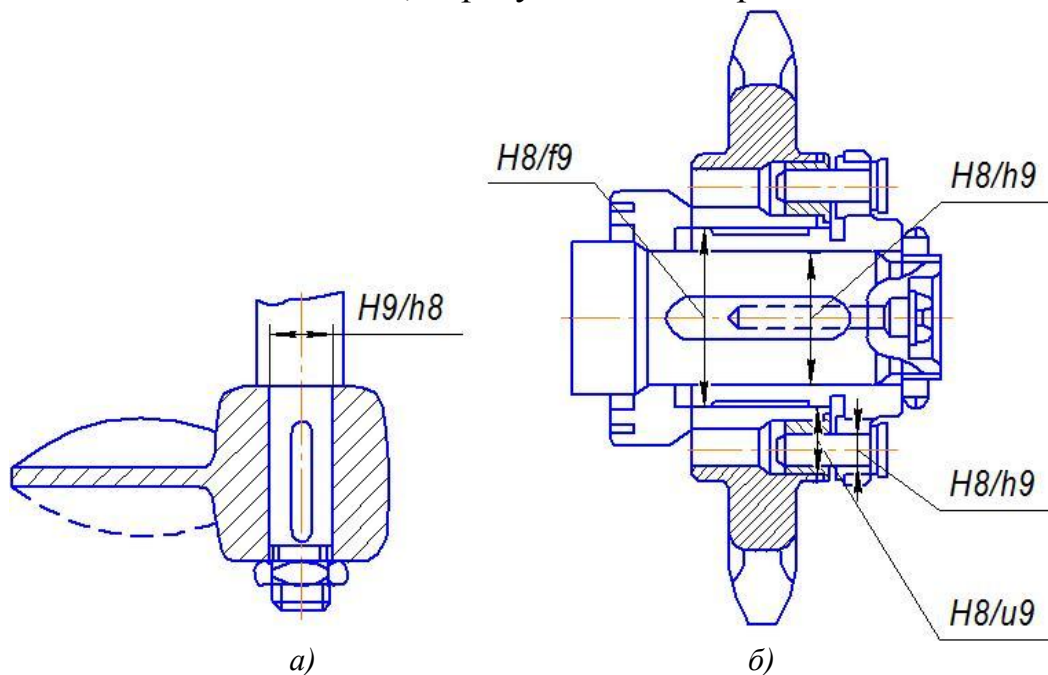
Посадки для нерухомо закріплюваних деталей:
